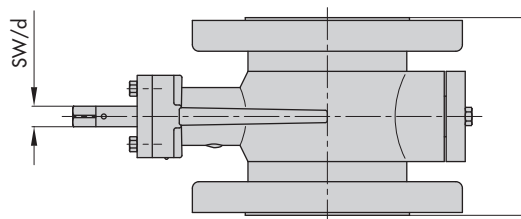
Disegno dimensionale Tipo 3310/3278
